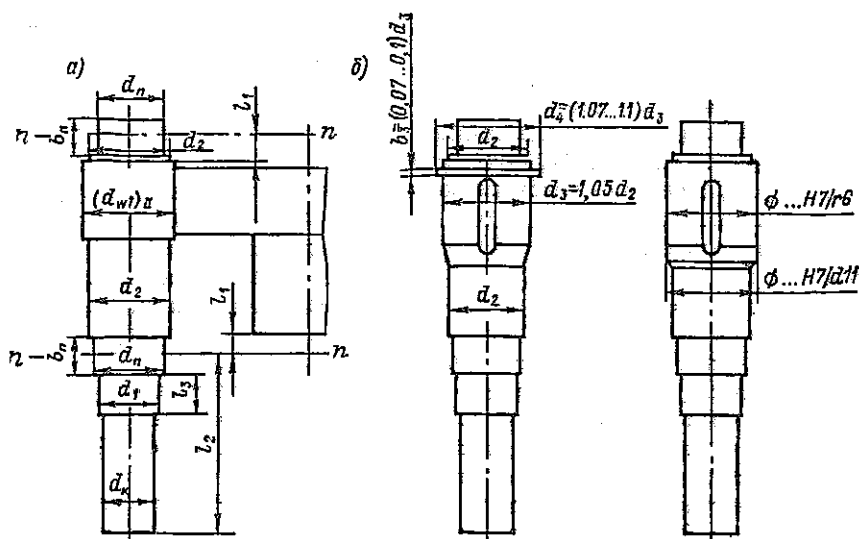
Компоновка быстроходного вала цилиндрического редуктора
